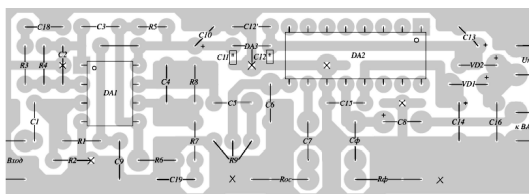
Эскиз платы УЗЧ – 2. Вид со стороны установки деталей. Крестами обозначены проволочные перемычки между фольгой общего провода с обеих сторон платы. Конденсаторы C11' и C12' – SMD, типоразмер – 0805...1206 устанавливаются со стороны печатных проводников.
